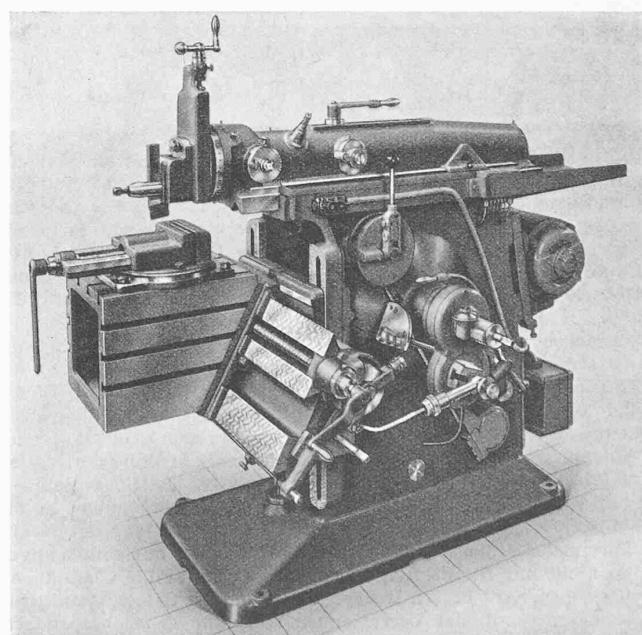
Schaeerer-Schnellhobler — Schweiz. Werkzeugmaschinen A. G.
